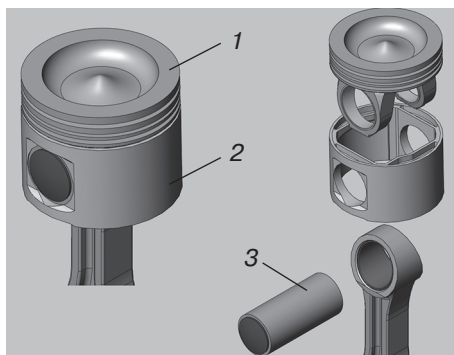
Конструкция рассматриваемого поршня: 1 — головка поршня; 2 — юбка; 3 — палец
